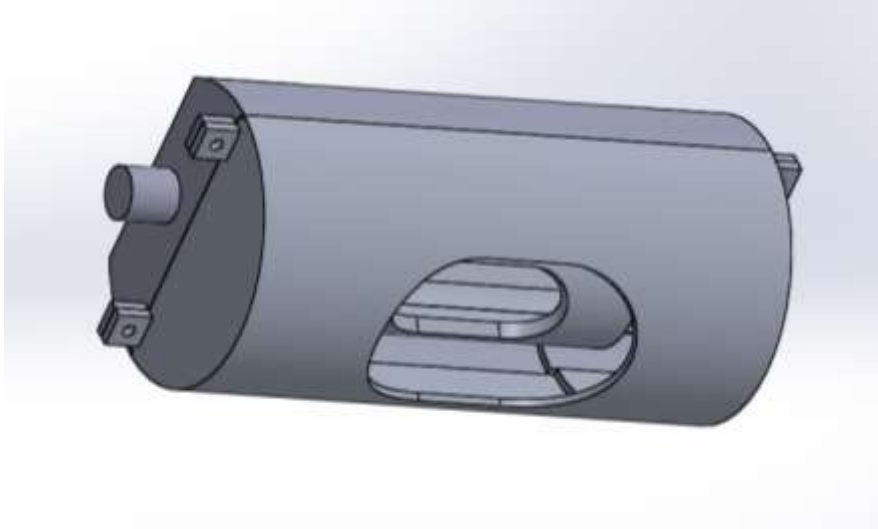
Prototipo a manufacturar en impresora 3D CUBE
